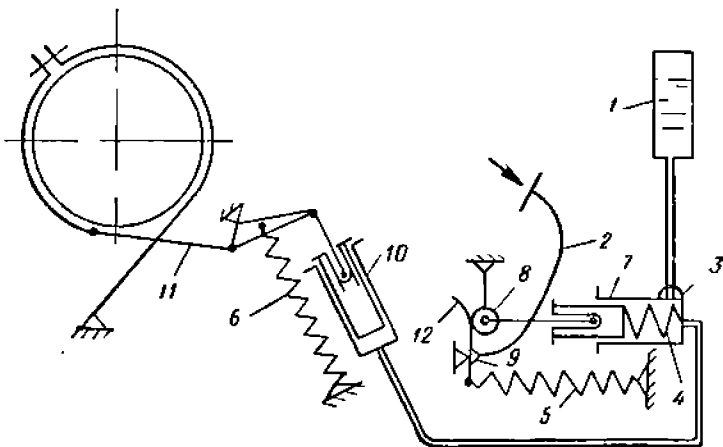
Схема гидравлического безнасосного управления тормозом лебедки: 1 — бак; 2 — педали; 3 — игольчатый клапан; 4, 5, 6 — возвратные пружины; 7 — цилиндр-датчик; 8 — ролик штока; 9 — ось вращения педали и кулачка; 10 — рабочий цилиндр; 11 — тяга ленты тормоза; 12 — кулачок
